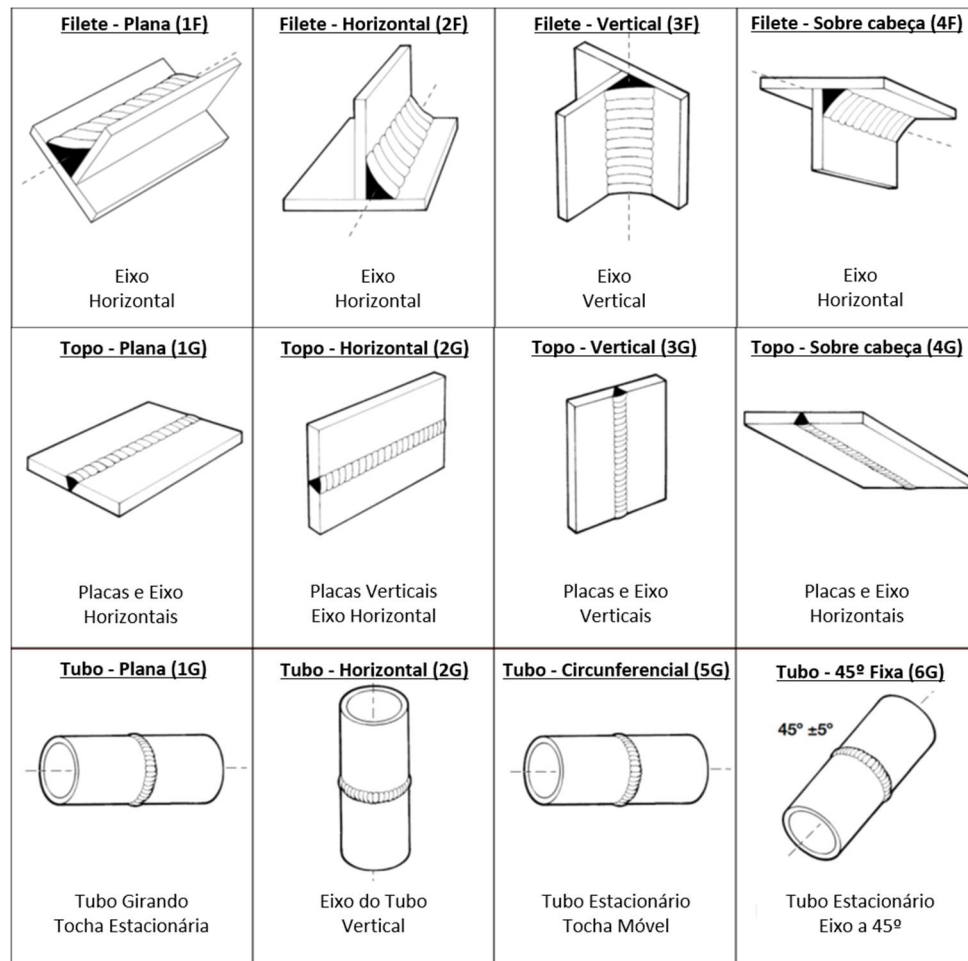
Posições de soldagem. Adaptado (HIWT, 2012, p. 36).
